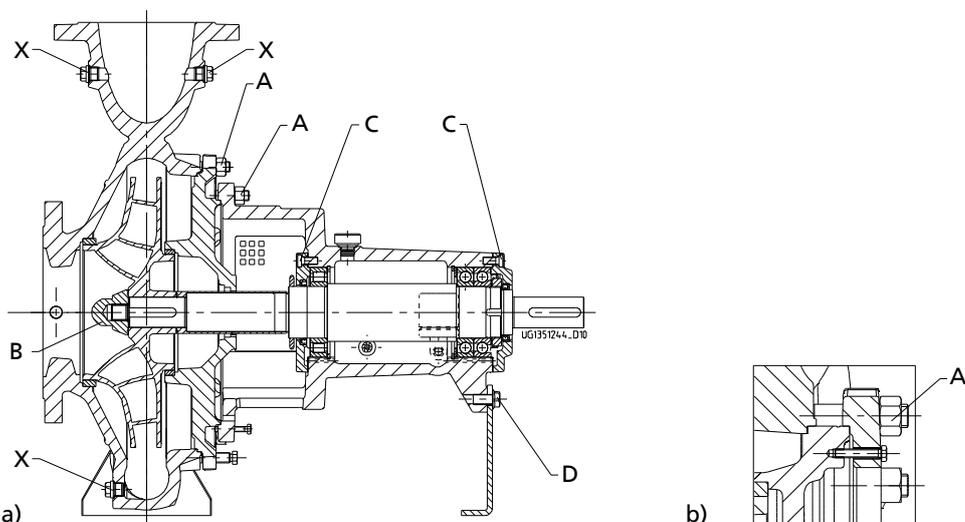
а) Места затяжки резьбовых соединений насоса, б) исполнение с зажимной крышкой корпуса
